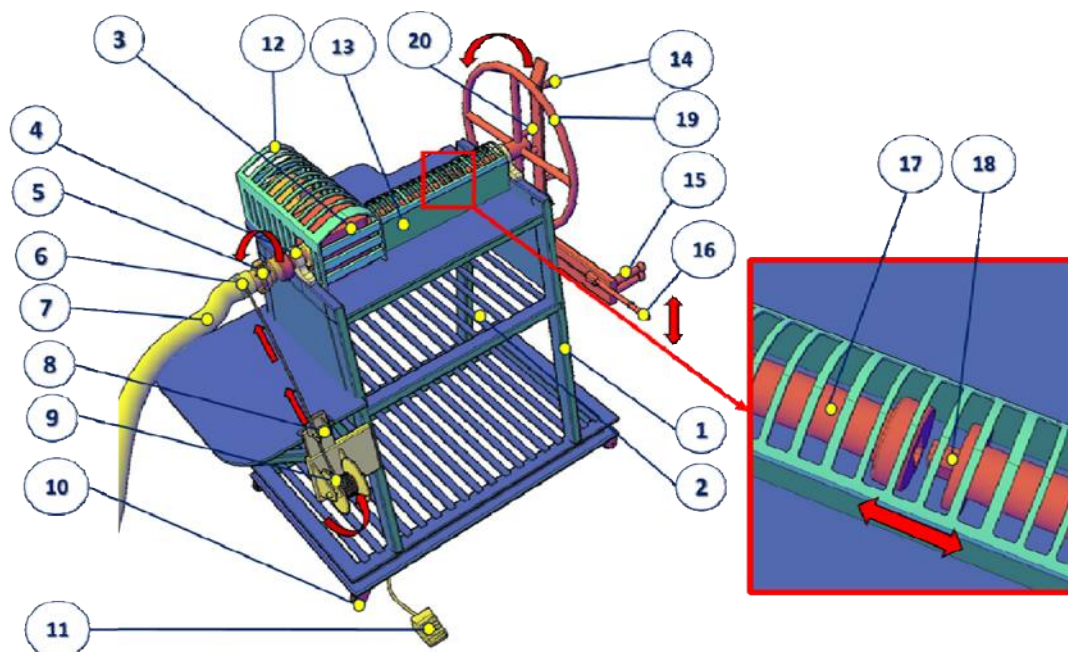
Комбинированный станок для обслуживания пожарных рукавов: 1 - рама станка; 2 - полка для хранения принадлежностей; 3 - привод; 4 - опора тихоходного вала; 5 - соединительная рукавная головка; 6 - проволока вязальная стальная; 7 - рукав напорный пожарный; 8 - ролик направляющий; 9 - кронштейн с катушкой; 10 - роликовые колеса фиксатором; 11 - выключатель ножной (педаль); 12 - защитный кожух привода; 13 - защитный кожух вала; 14 - колесо со спицами; 15 - ригели направляющие; 16 - рычаг подвижный; 17 - вал тихоходный; 18 - соединитель валов; 19 - колесо со спицами; 20 - штырь со съемной втулкой и прижимом
